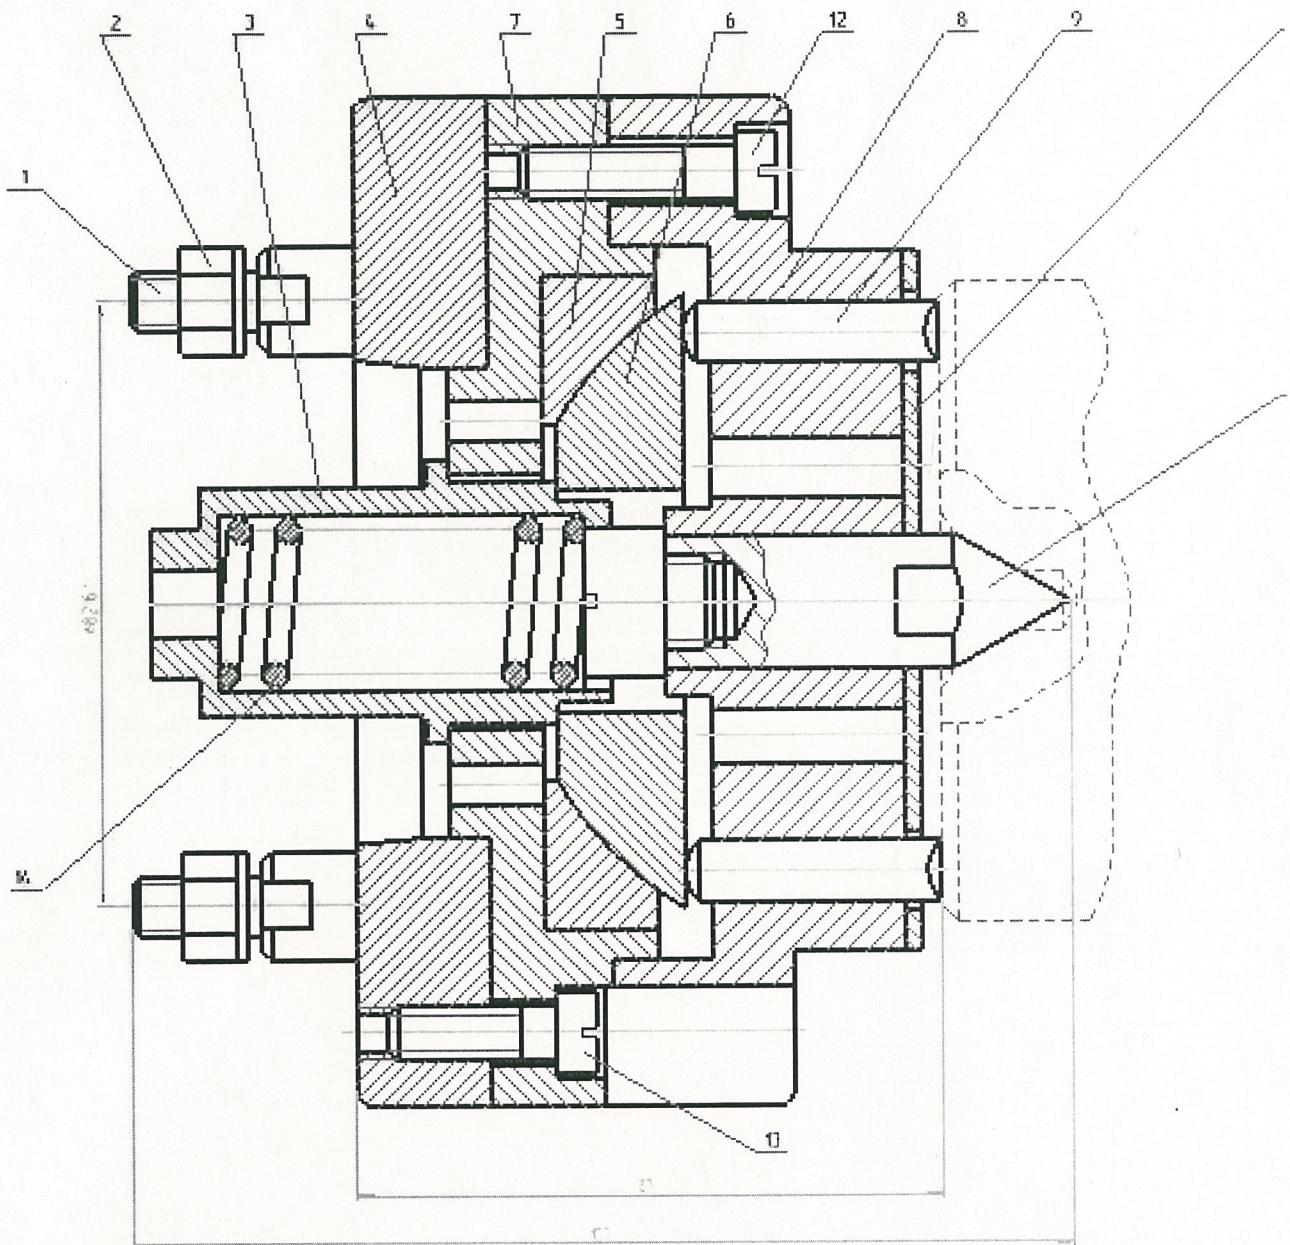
Повідковий патрон для тонкої токарної обробки валу
